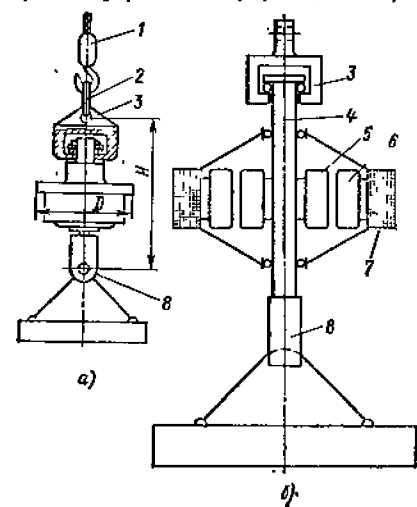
Поворотное ГУ фирмы Пайнер: а — общий вид; б — схема привода
